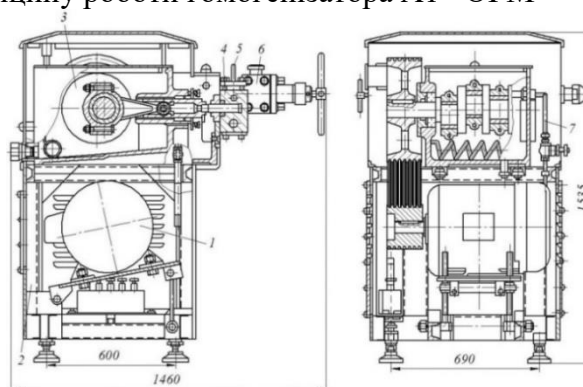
Конструкція гомогенізатора А1- ОГМ 1 – електродвигун; 2 – станина; 3 – кривошипно - шатунний механізм; 4 – плунжерний блок; 5 – манометрична головка; 6 – гомогенізуюча головка; 7 – система змащення та охолодження.
